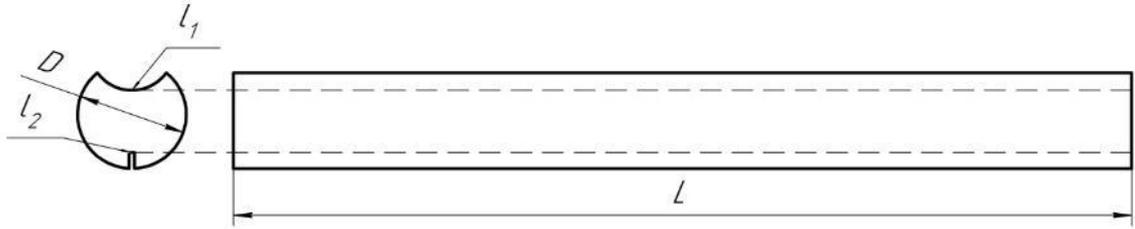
Основные размеры заготовки:  $D$  – диаметр заготовки;  $L$  – длина заготовки;  $l_1$  – продольный паз;  $l_2$  – продольный технологический пропи
